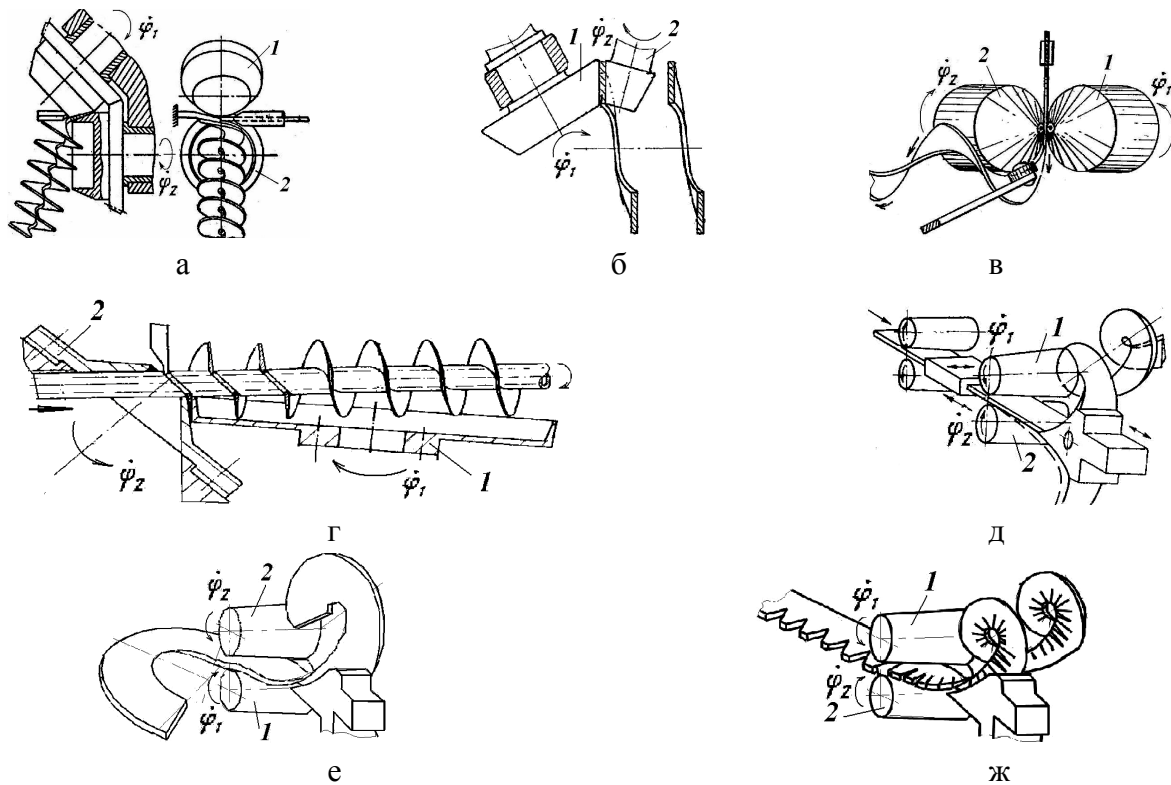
Схеми формоутворення ГЗ методом прокатування за допомогою інструментів з конусними робочими поверхнями:
